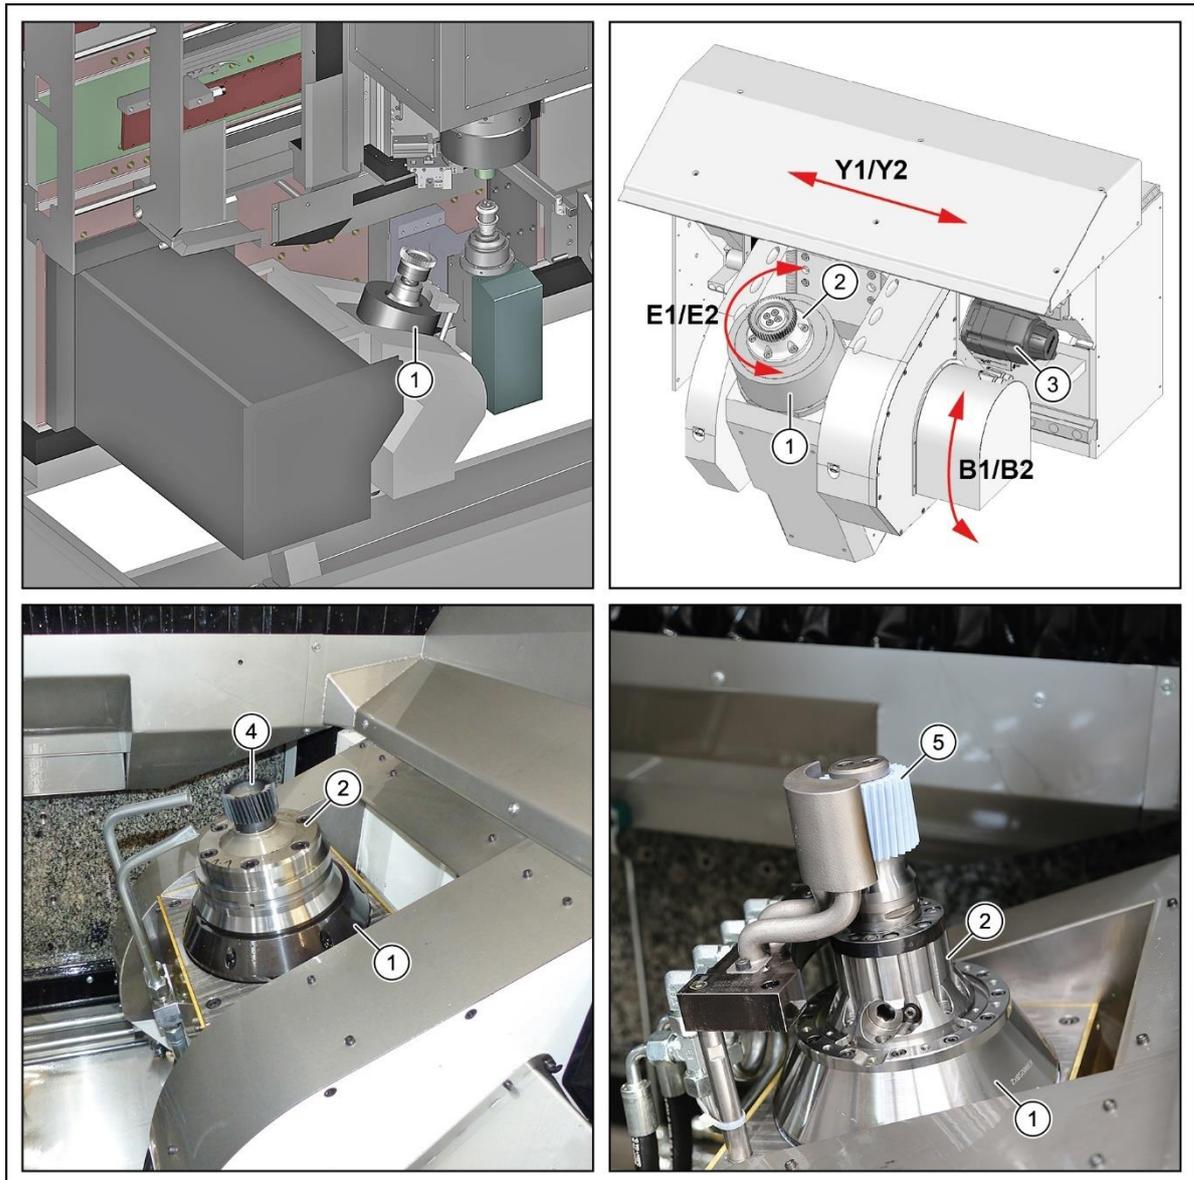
Werkzeugspindel E1/E2 - Wälzschälmodule - SynchroForm (Beispiel)
